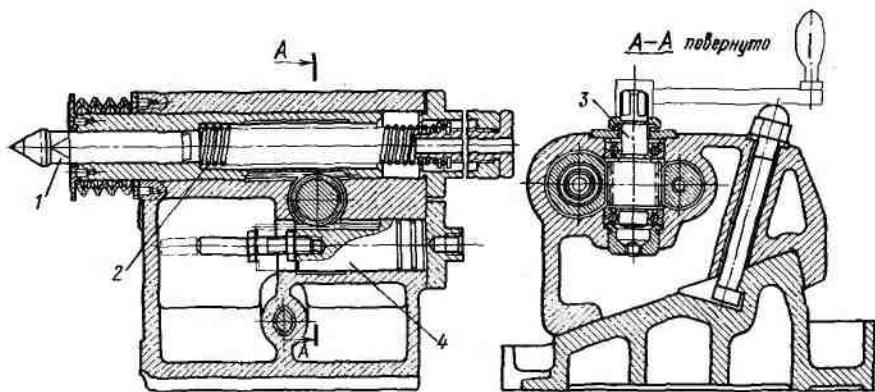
Конструкция задней бабки круглошлифовального станка
